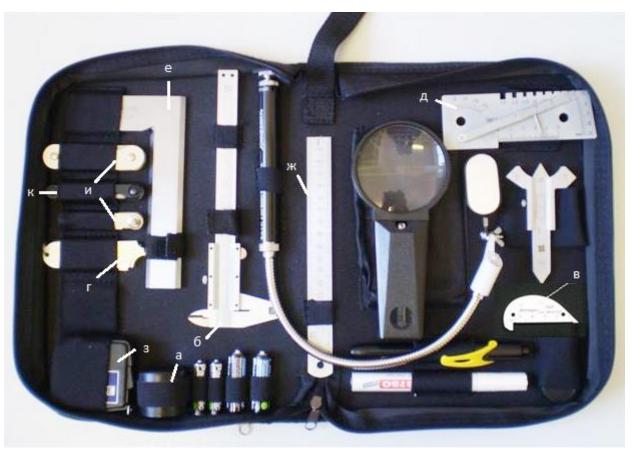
Комплект для визуально измерительного контроля: а - лупа измерительная ЛИ 10х; б – Штангенциркуль ШЦ-1-125-0.1; в - Универсальный шаблон Красовского УШК-1; г - Универсальный шаблон сварщика УШС-2; д - Универсальный шаблон сварщика УШС-3; е - Угольник поверочный; ж - Линейка измерительная металлическая; з – рулетка 5 м; и — наборы радиусных шаблонов №1, №3; к — Набор щупов №4;
